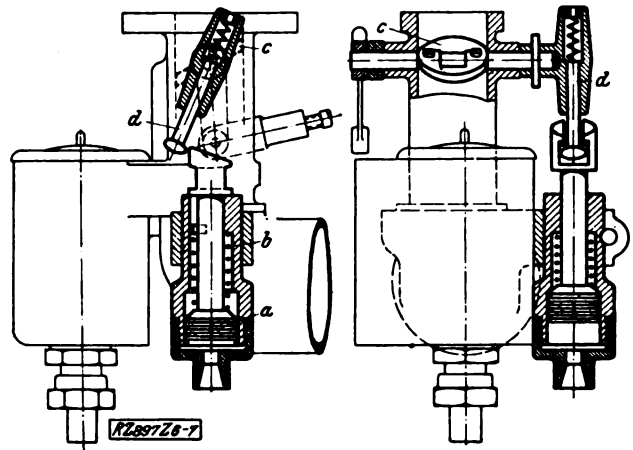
und 6. Sicherung gegen das Versagen der Schmierung.
